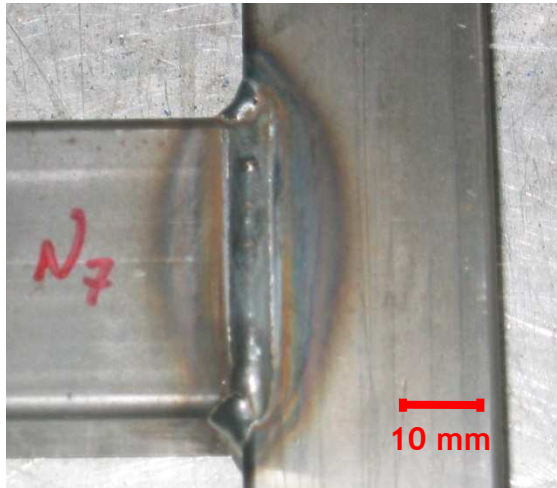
IMAGEM REPRESENTATIVA DOS CORDÕES DE SOLDADURA EFECTUADOS COM O PROGRAMA B
